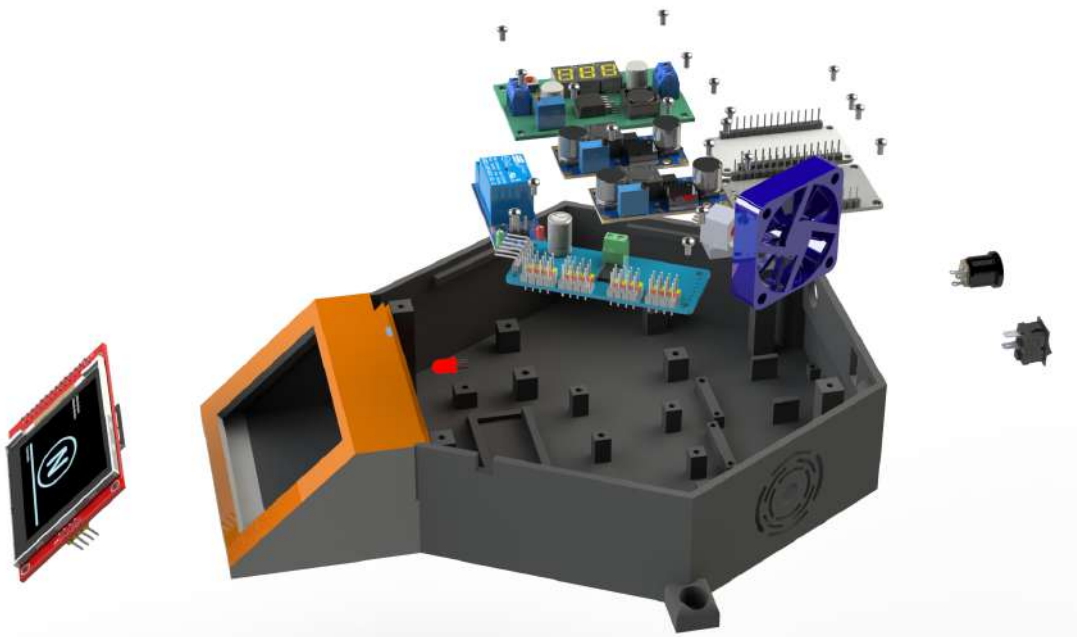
CAD del diseño electrónico explosionado. Fuente: Elaboración propia
